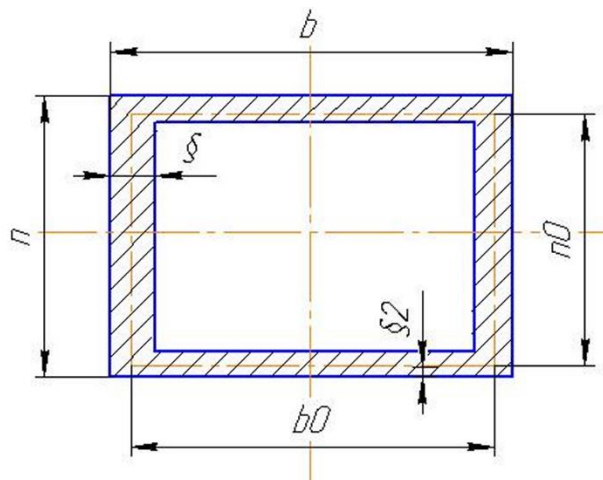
Розрахункова схема балки (поперечний переріз)
